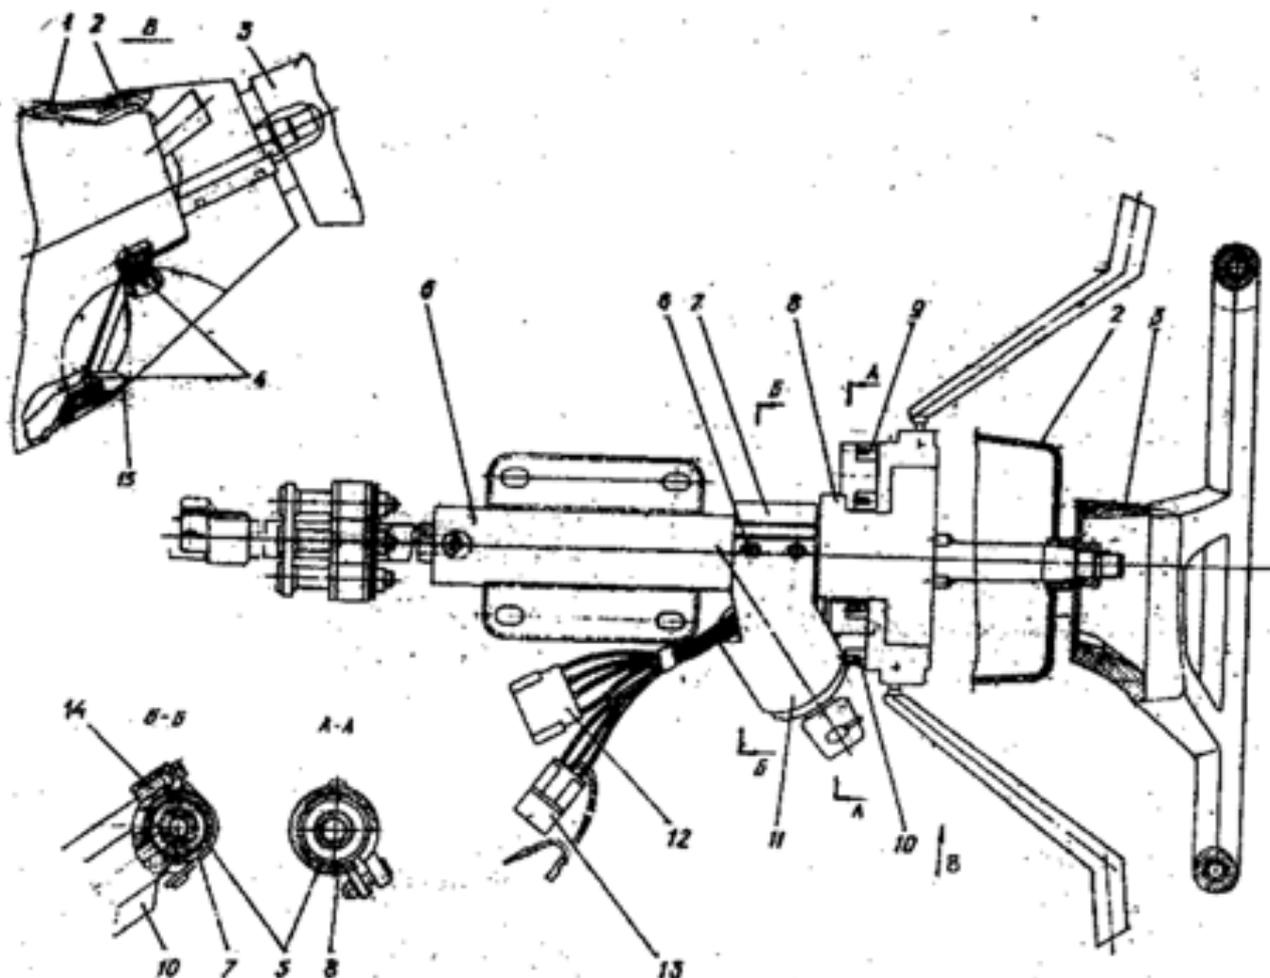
Опора вала в сборе (с двухрычажным переключателем): 1 - панель приборов; 2 - кожух верхний; 3 - колесо рулевое; 4 - винт; 5 - опора вала; 6 - головка болта; 7 - скоба; 8 - переключатель в сборе; 9 - колодка стеклоочистителя; 10 - колодка световой сигнализации; 11 - выключатель зажигания; 12 - колодка к жгуту проводов; 13 - реле замка зажигания; 14 - болт; 15 - кожух нижний.
